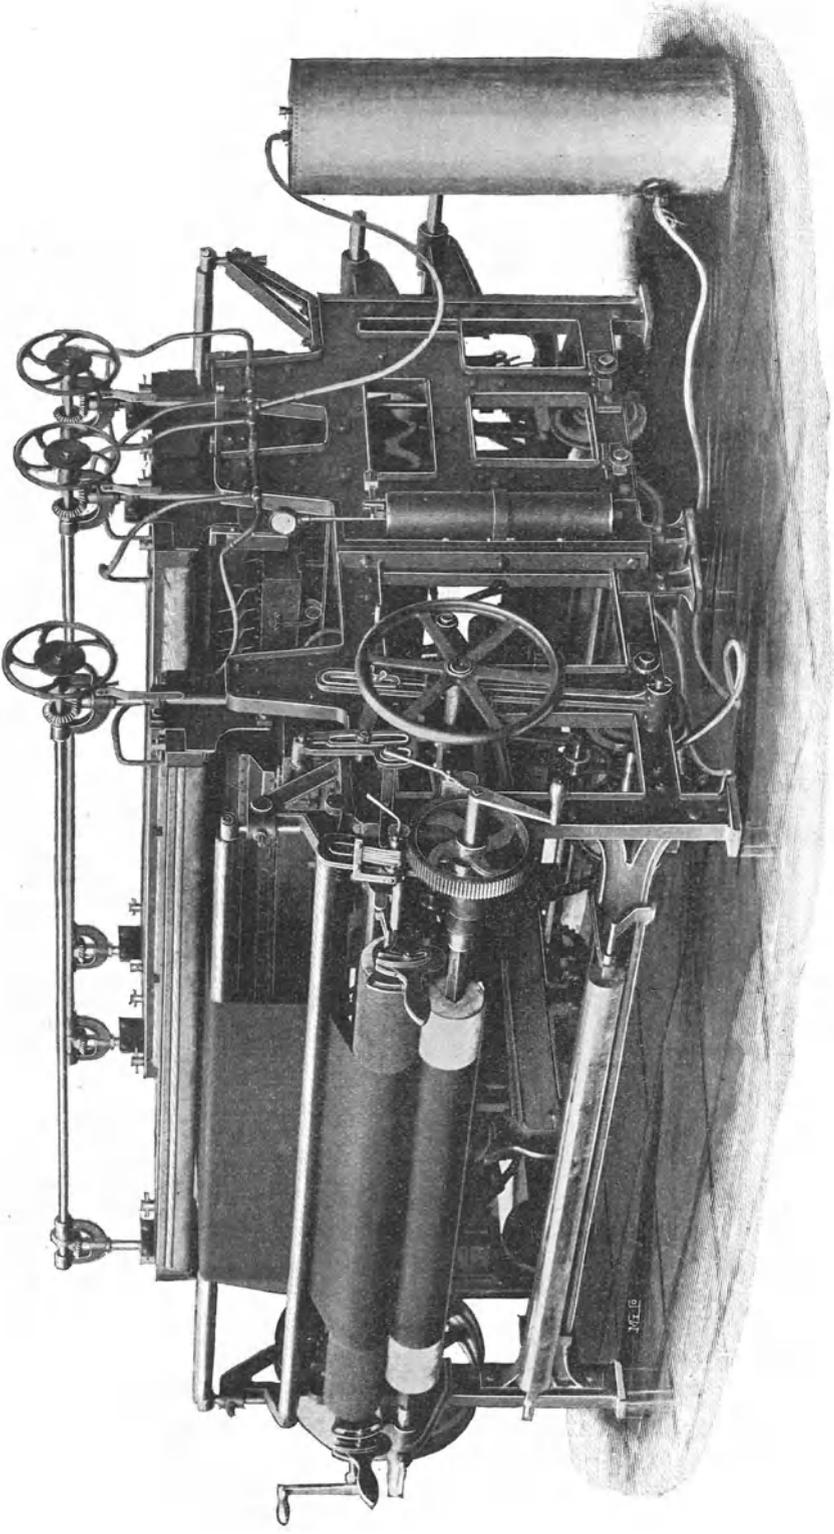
Universal-Stoffreibmaschine von Schweizer.
